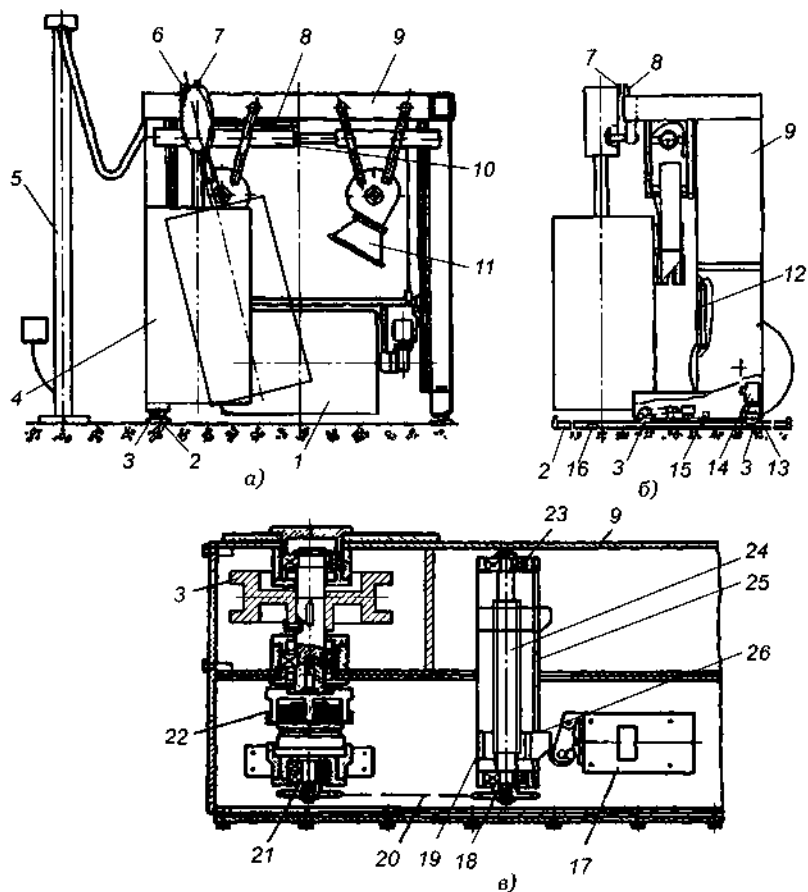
Щеточная моечная установка с устройством для обдува (сушки) автомобиля: *а* — общий вид; *б* — устройство вертикальной щетки; *в* — устройство для перемещения установки; 1 — горизонтальная щетка; 2 — рельс; 3 — опорный ролик; 4 — вертикальная щетка; 5 — стойка; 6 — бесконтактный датчик; 7 — пластина; 8, 10, 12 — пневмоцилиндры; 9 — рама; 11 — вентилятор; 13 — редуктор; 14 — электродвигатель; 15 — упор; 16, 17 — конечные выключатели; 18, 21 — звездочки; 19 — гайка; 20 — цепная передача; 22 — электромагнитная муфта; 23 — подшипник; 24 — ходовой винт; 25 — направляющая; 26 — упор
